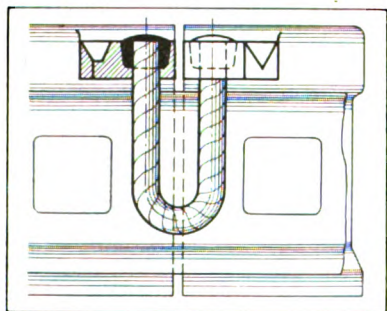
Anschweißbarer Kupferverbinder mit angeschweißten Eisensternen.
